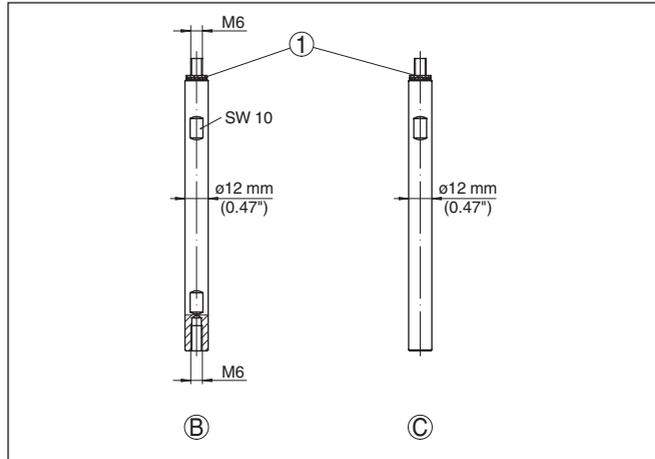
Componentes de varilla con \varnothing 12 mm (0.47 in)
